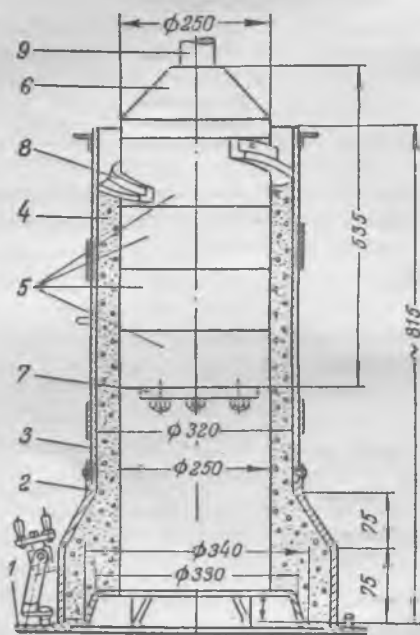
Металлическая форма для изготовления труб (со шпинделем станка). 1 — поддон; 2 — растроб; 3 — колесо; 4 — бетонная масса трубы; 5 — секция трамбовки; 6 — конус трамбовки; 7 — днище трамбовки; 8 — спиральный гребень; 9 — шпиндель.
